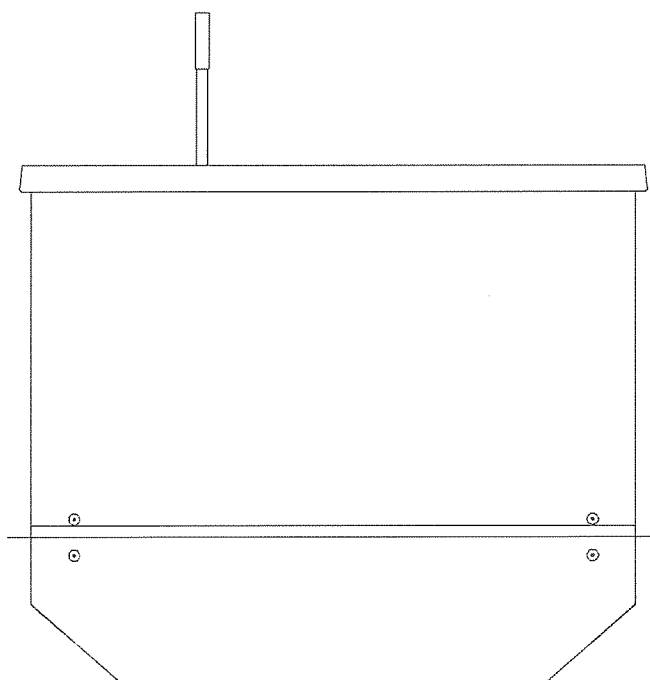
Elewacja prawa stacji (strona frontowa)
